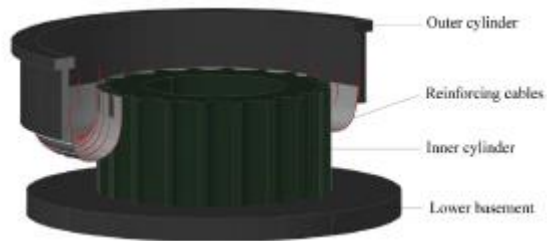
Schema cable reinforced air spring (Zhou et al., 2016)
